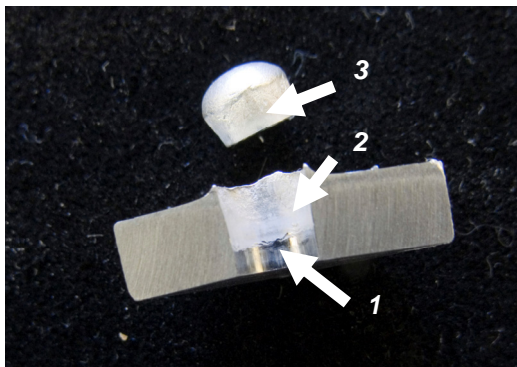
Внешний вид поверхности разрушения и пробки. Зеркальная и шероховатая поверхности разрушения на образце обозначены цифрами 1 и 2 соответственно; пробка – 3
